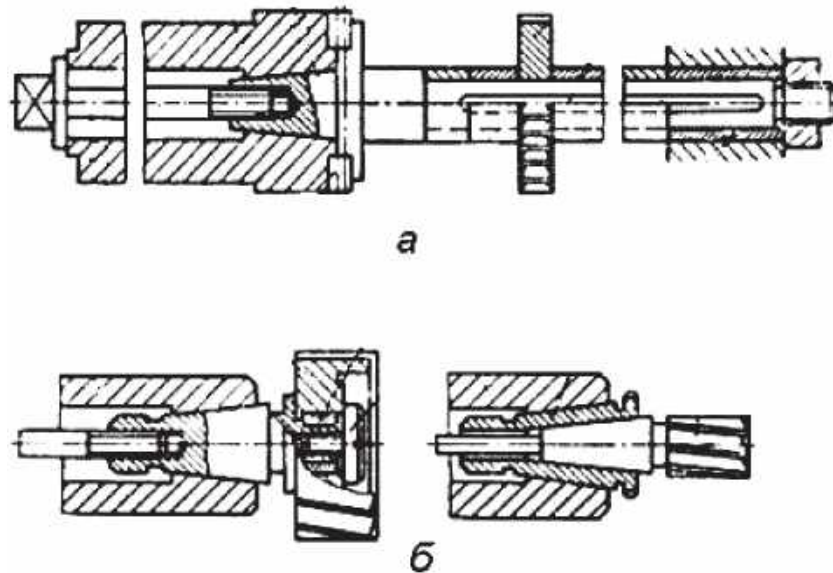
Оправки для фрез: а – довга; б – кінцева
